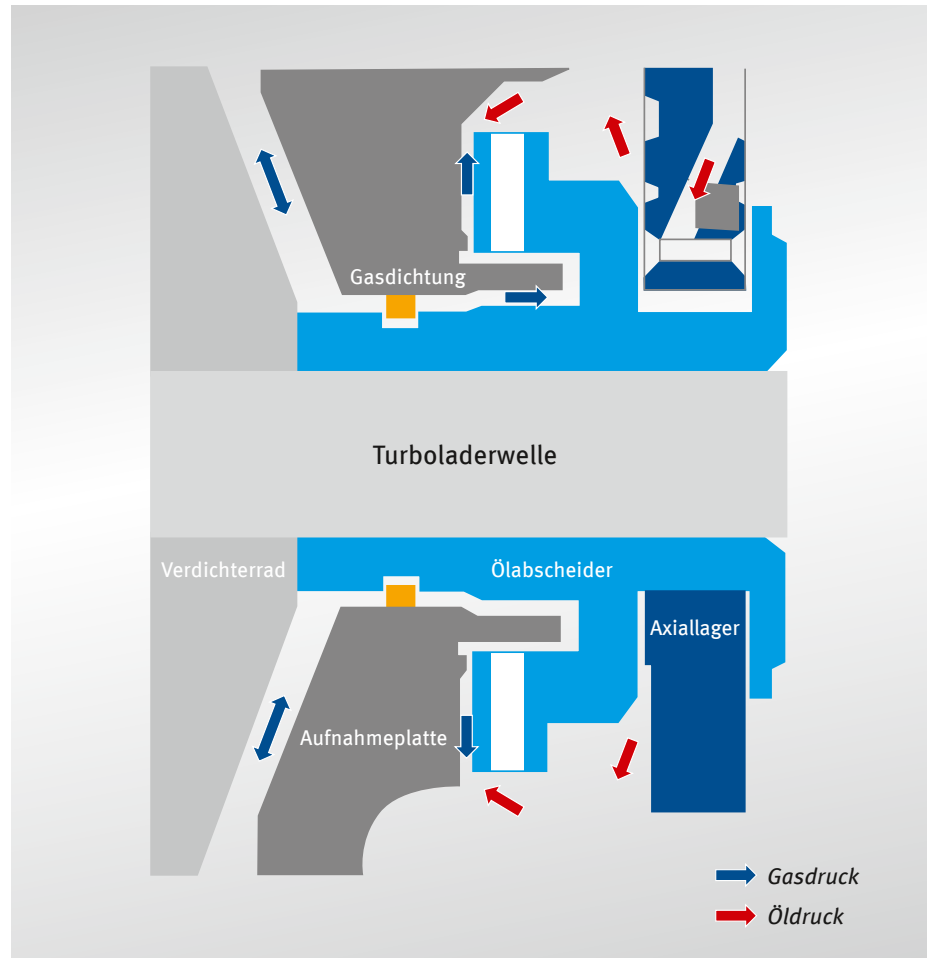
Die Turbinenwelle „schwimmt“ auf einem Ölfilm
